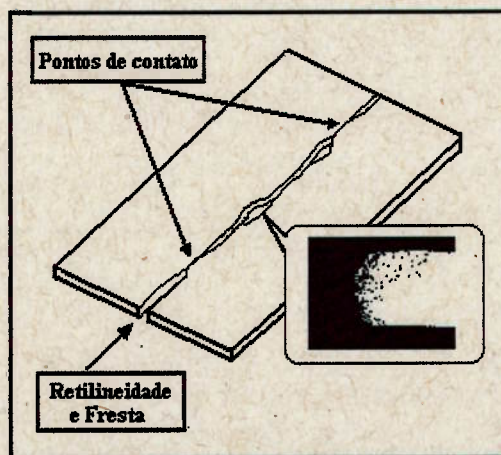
Exemplos de defeitos na superfície de corte [Pincinini99].
